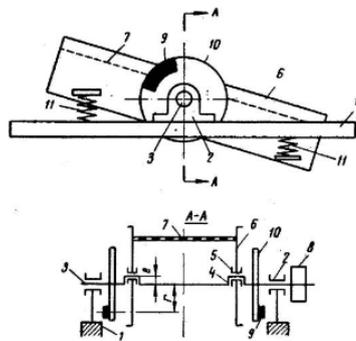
Общий вид (а) и кинематическая схема (б)
